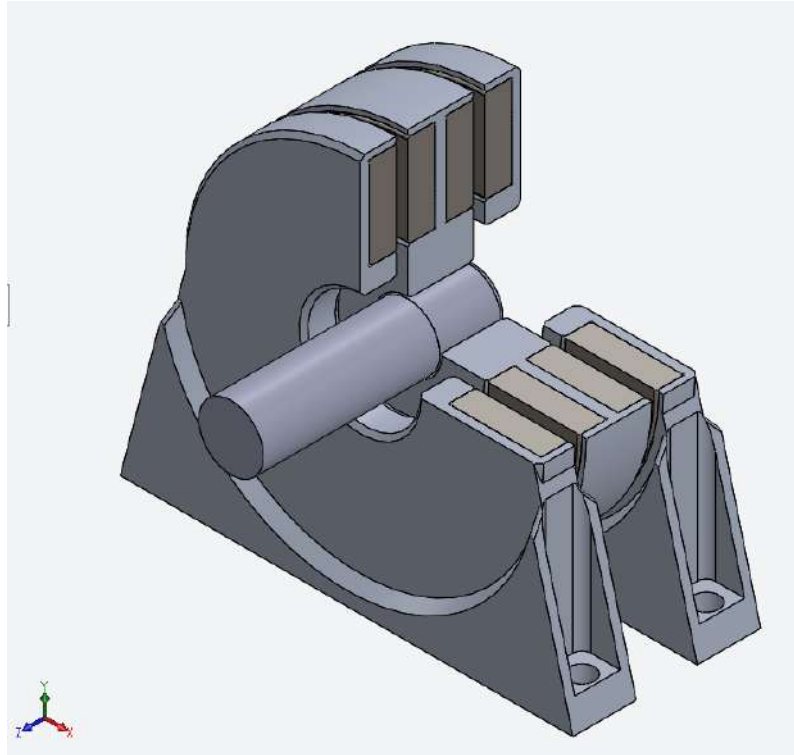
Vista isométrica em corte de meia-seção do mancal magnético axial passivo de magnetização axial.
